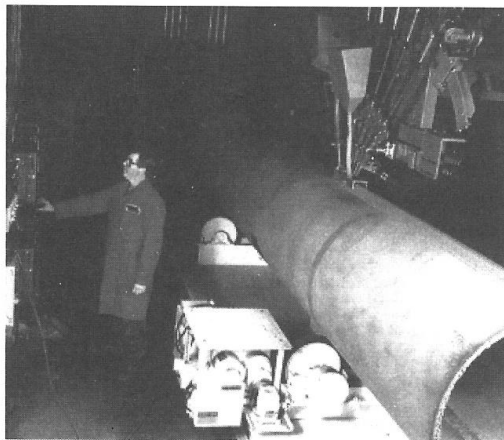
Fabricación de tuberías mediante soldadura automática por arco sumergido que emplea cinco alambres simultáneamente.
